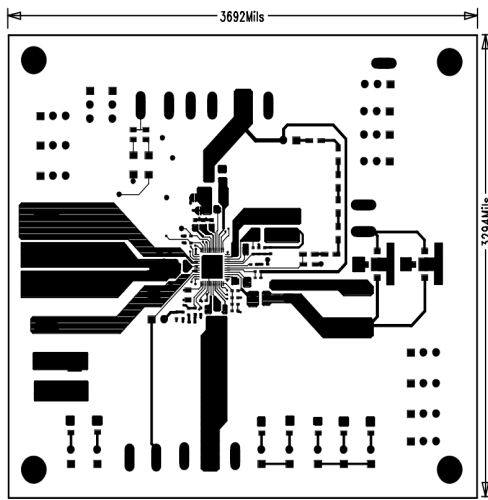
Max 8662 PCB LayOut - Top Layer 1.
